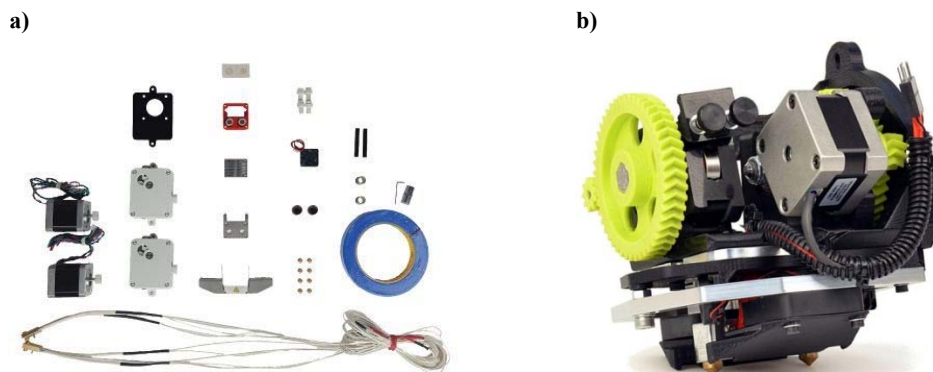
a) Kit de peces per incorporar doble extrusió en un capçal. b) Kit dual extruder de Lulzbot. Font: [166, 167].
